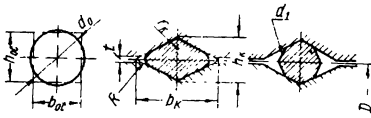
Двухкратная вальцовка заготовки в ромбическом ручье
